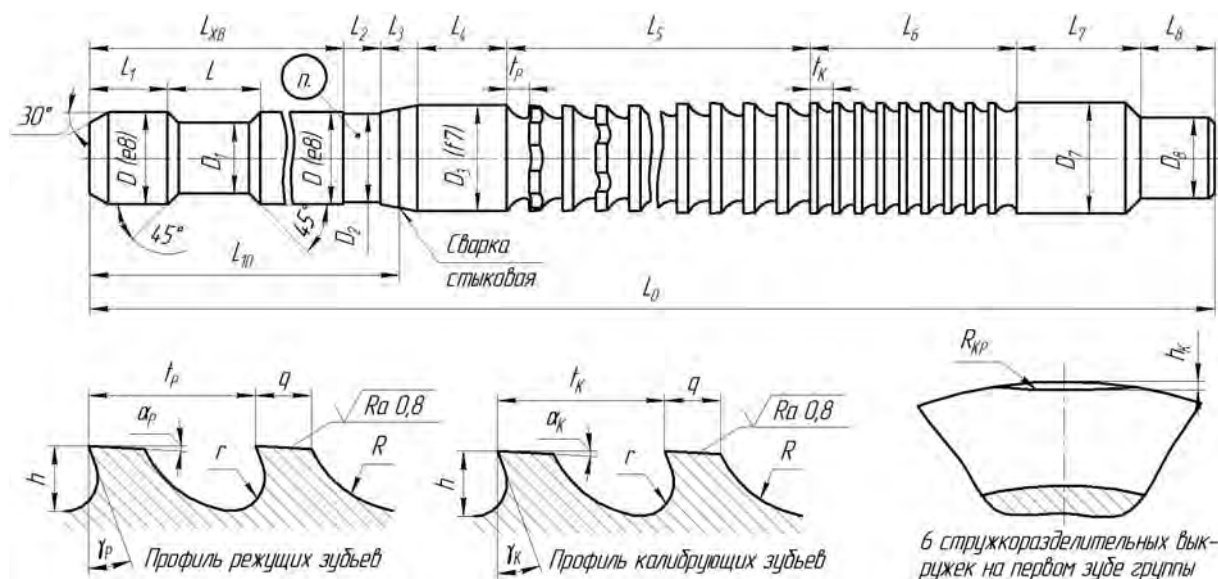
Протяжка для обработки цилиндрического отверстия
